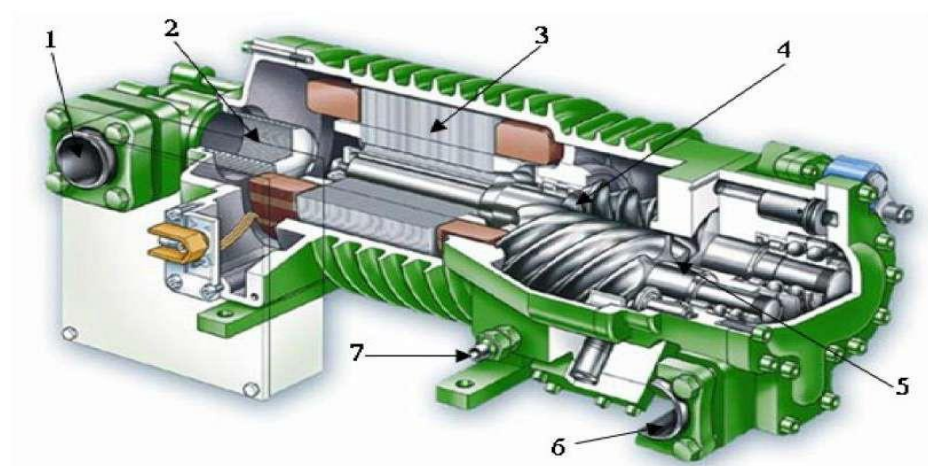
Винтовой компрессор: 1 – всасывающий патрубок; 2 – сетчатый фильтр; 3 – обмотка электродвигателя; 4 – полость между зубьями; 5 – пар и масло проходит вдоль вала до нагнетательного фланца; 6 – нагнетательный патрубок; 7 – патрубок возврата масла
